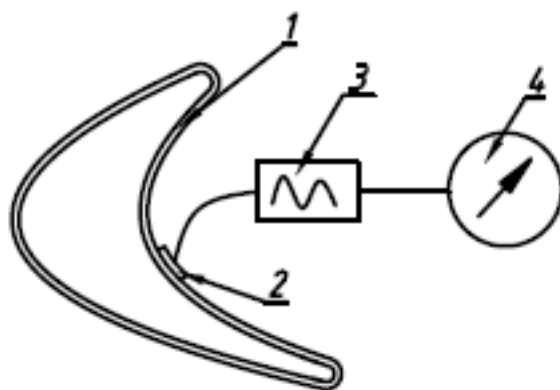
Схема контроля толщины стенок лопатки: 1 – лопатка; 2 – ультразвуковой излучатель/приемник; 3 – аналого-цифровой преобразователь; 4 – индикатор
